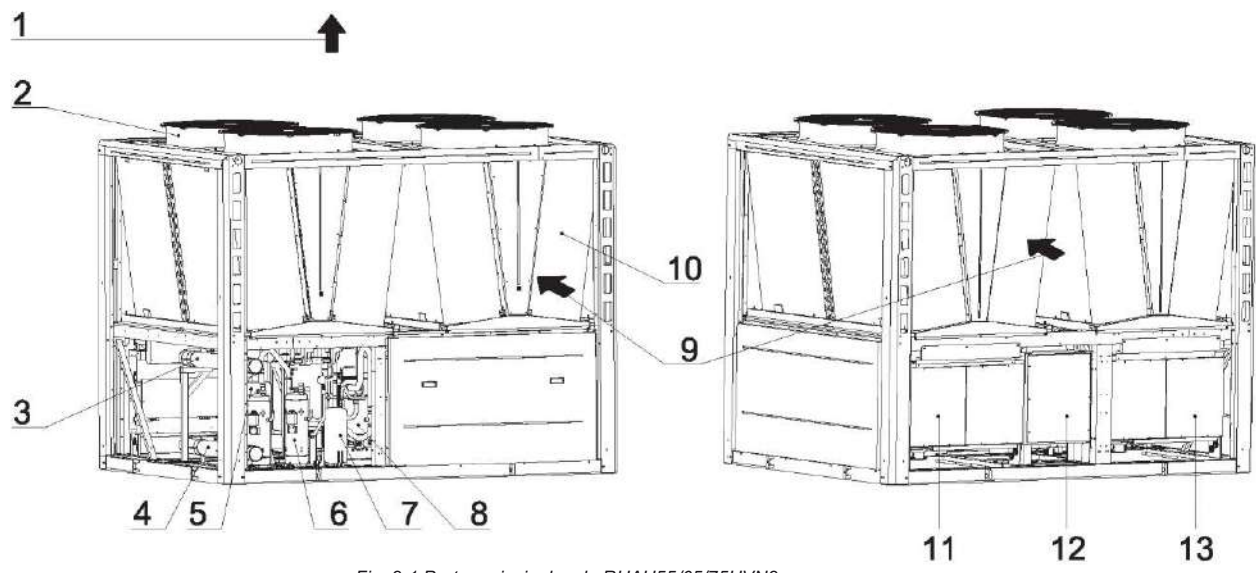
Partes principales de RHAH55/65/75HVN8
